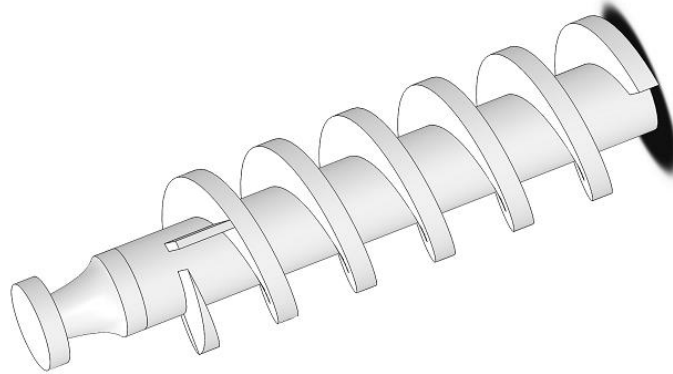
Ensamble del tornillo 1 junto con su reductor.
